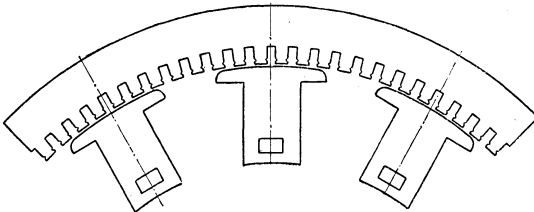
Blechschnitt einer Wechselstrommaschine.
